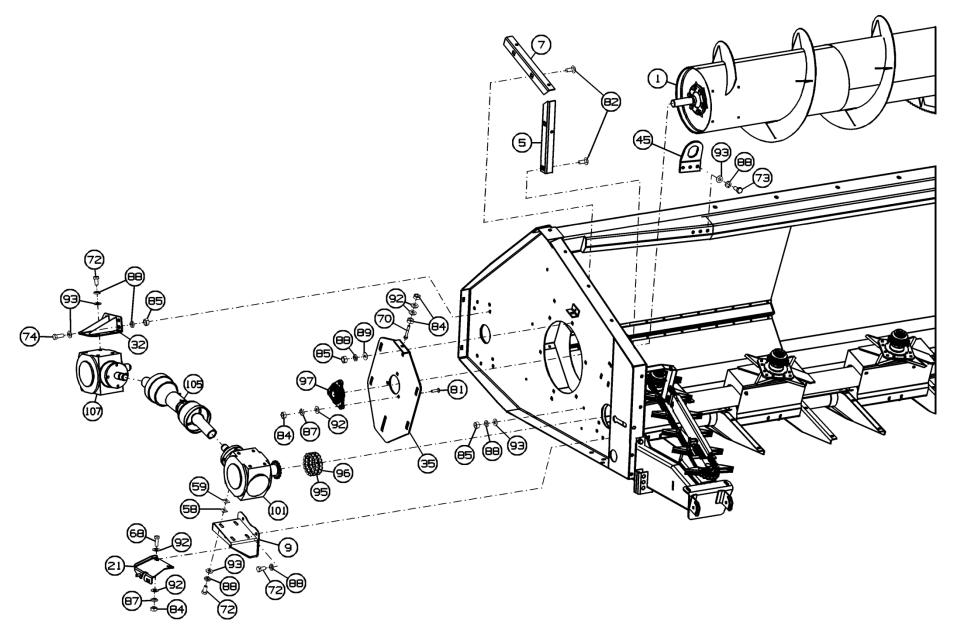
Корпус жатки ПСП-620.01.01.000
